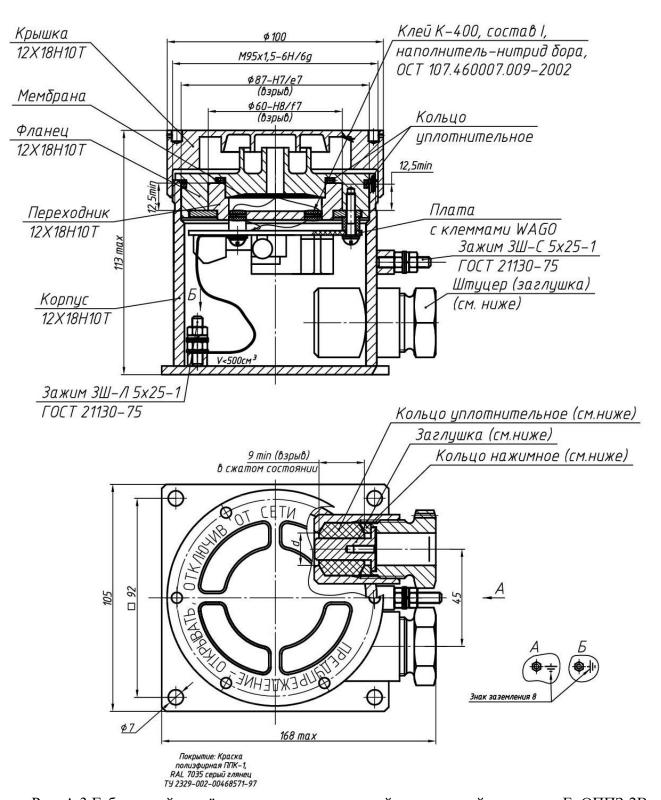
Габаритный чертёж звуковых оповещателей повышенной мощности ExOПП3-2В-ПМ-220-H, ExOПП3-2В-ПМ-H в нержавеющем корпусе, совмещённый с чертежом взрывозащиты. Маркировка показана в п. 1.6.
